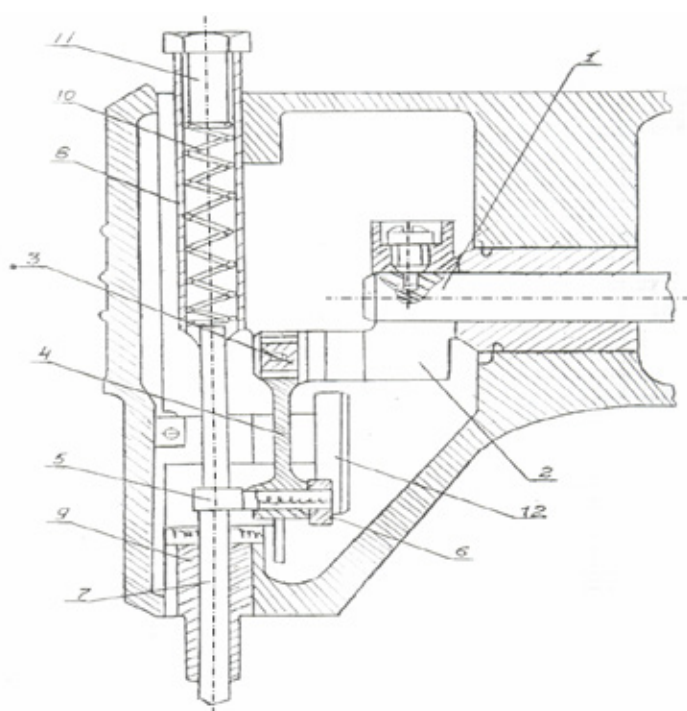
Совершенствованная конструктивная механизма иглы с упругими элементами: 1 — вал; 2 — кривошип; 3 — палец; 4 — шатун; 5 — поводка; 6 — ползун; 7 — игловодитель; 8, 9 — втулка; 10 — пружина; 11 — винт; 12 — паз
